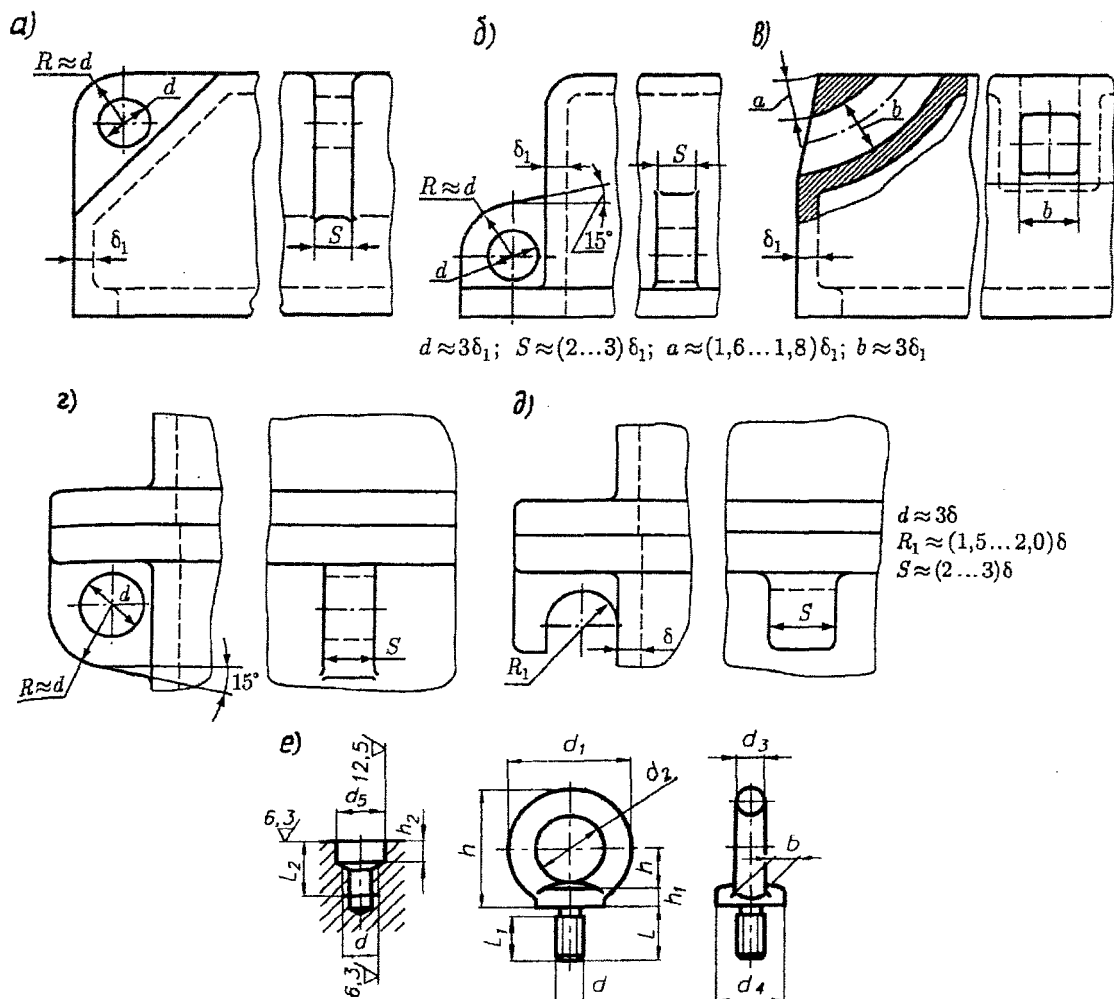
Устройства для подъема и транспортирования корпусных деталей и редуктора в сборе: а...в – проушины крышки; г...д – проушины корпуса редуктора; е – рым-болт
